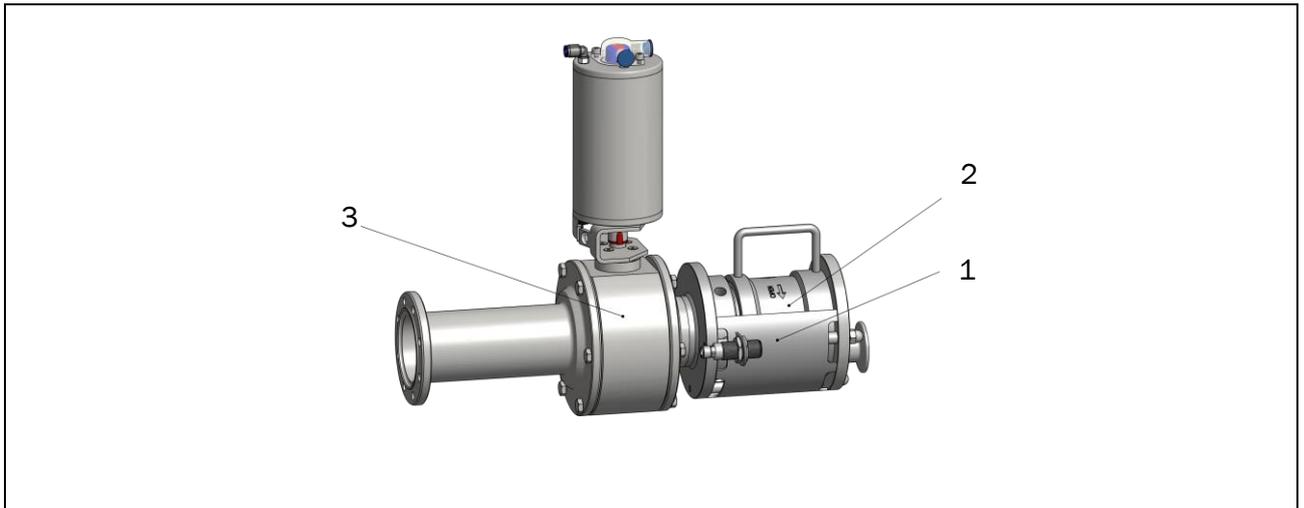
Übersicht Steckkammer mit Kugelventil
